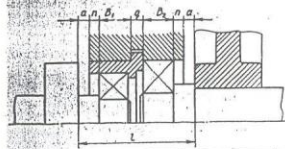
Компоновка подшипникового узла соосного редуктора
